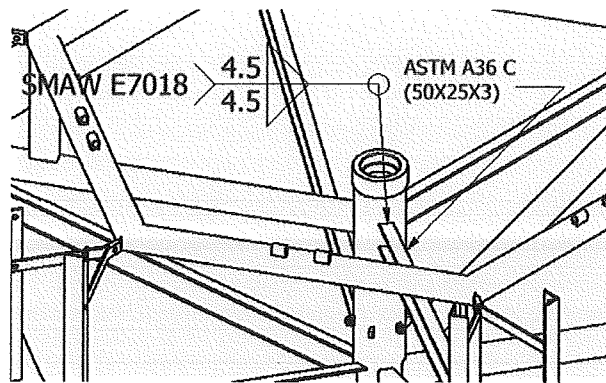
Detalle de Soldadura del Eje Principal parte Superior
